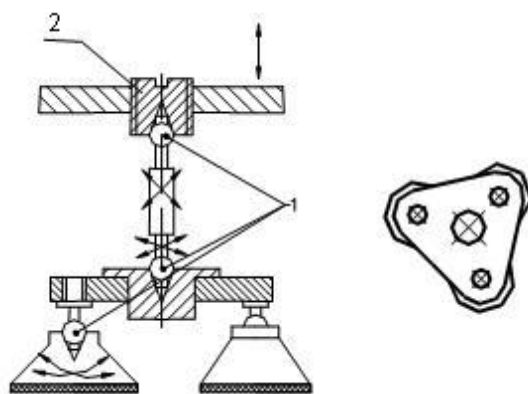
Самовстановлювана опора: 1 – шаровий шарнір; 2 – регулювання зусилля притиску
